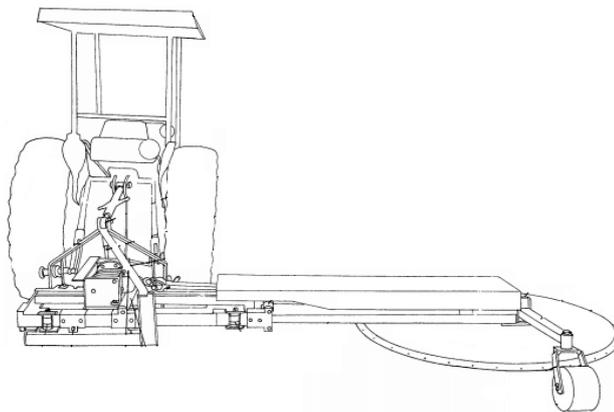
Desenho da disposição introduzida em roçadora conjugada.
